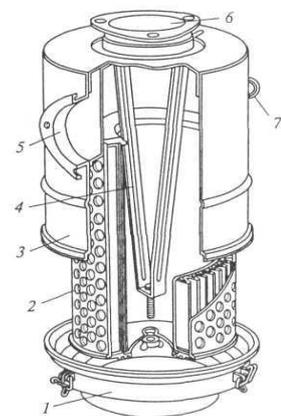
Воздушный фильтр: 1 - крышка; 2 - фильтрующий элемент; 3 - корпус; 4 - диффузор; 5, 6, 7 – патрубки
